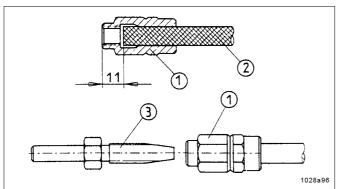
Prémontage des douilles filetées et des embouts pour tuyau sur la conduite principale
